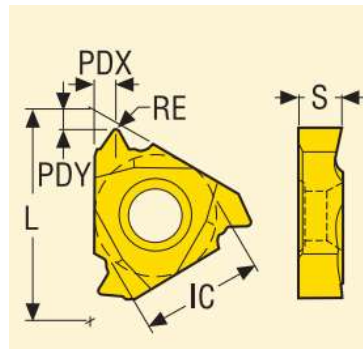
Форма пластины LCMF160608-0600-FT
